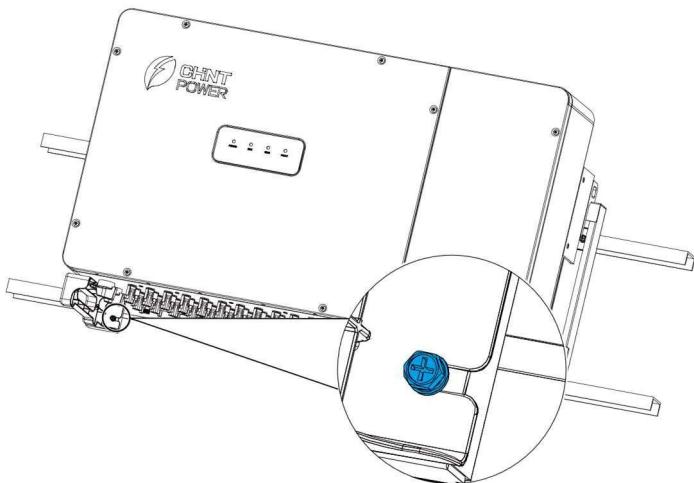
Inversor fixado no suporte do painel traseiro
